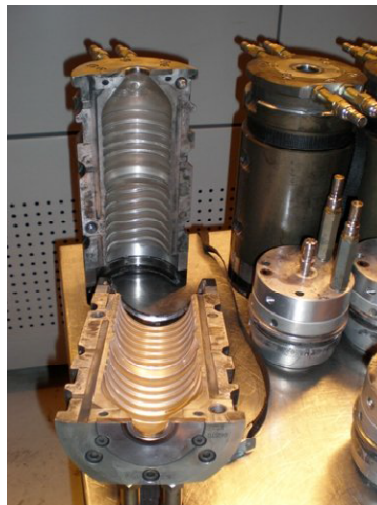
Moule ouvert dans lequel les préformes sont soufflées [2].
